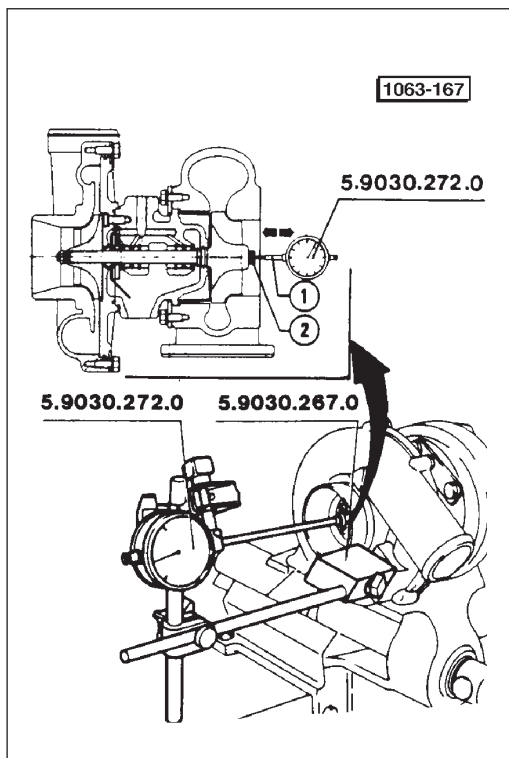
Contrôle du jeu axial de l'arbre rotor.
